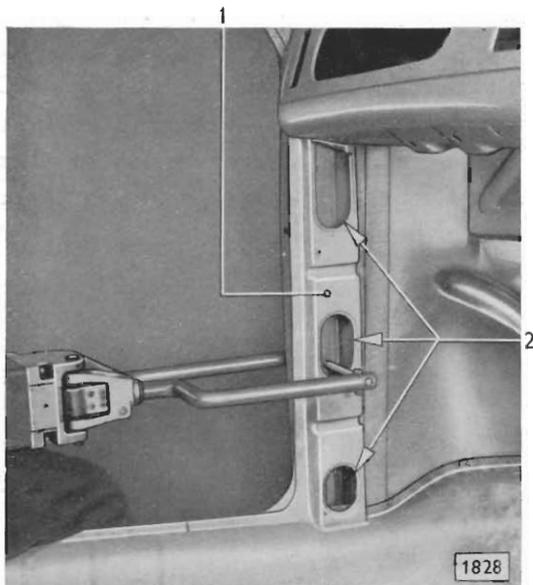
Vorderkotflügel an Karosserie-Scharniersäule punktschweißen
